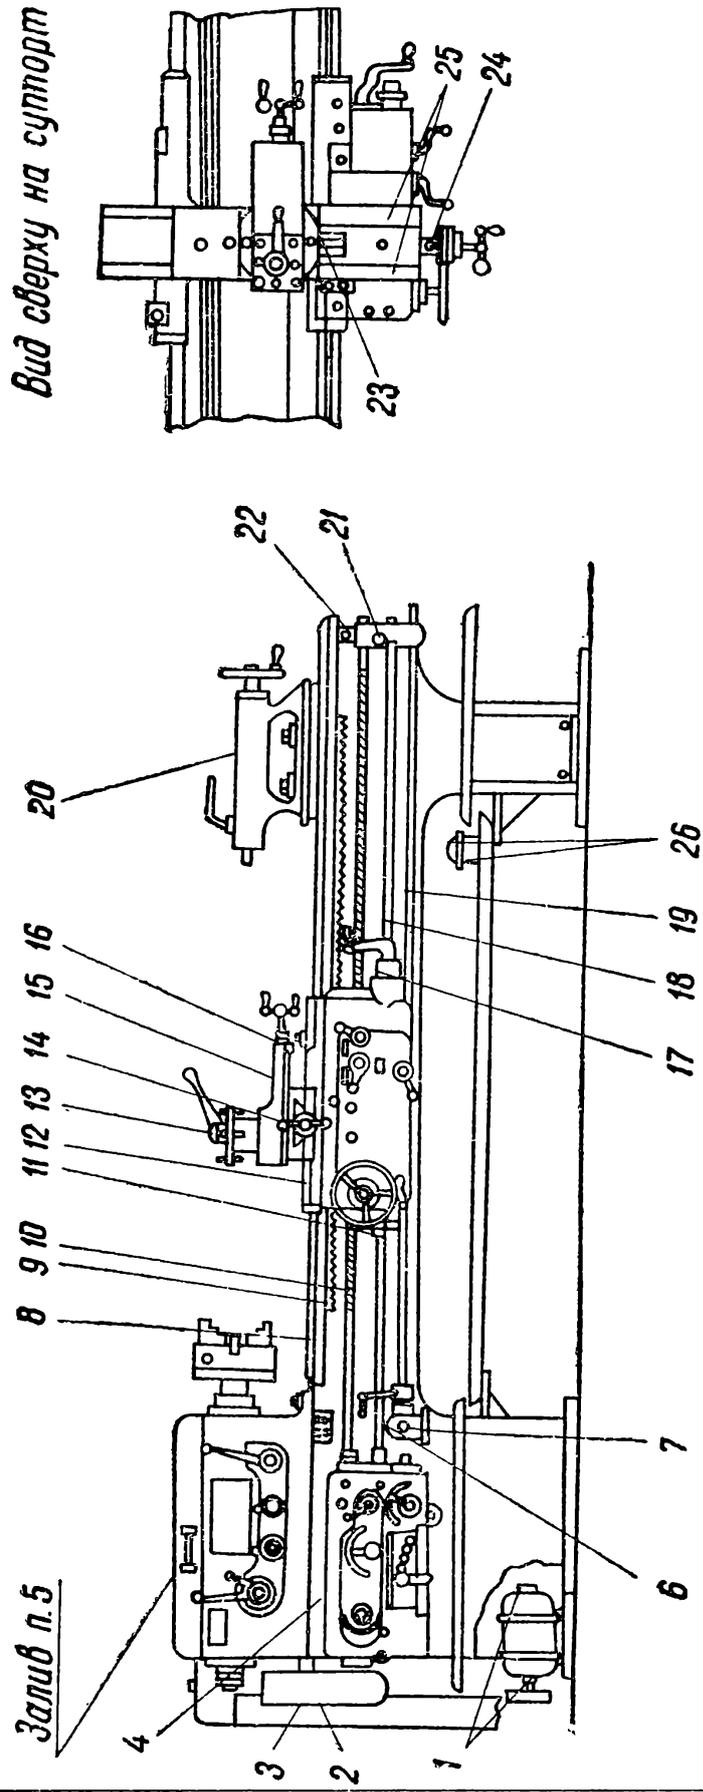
Карта смазки токарно-винторезного станка ДИП-200.
